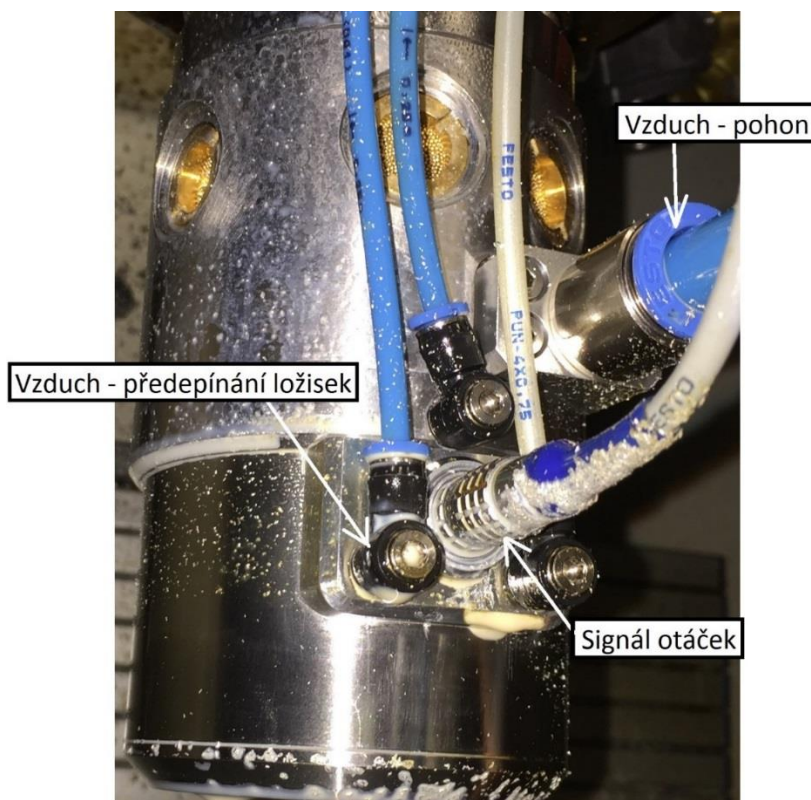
Laboratorní vřeteno ČVUT FS Ú12135
